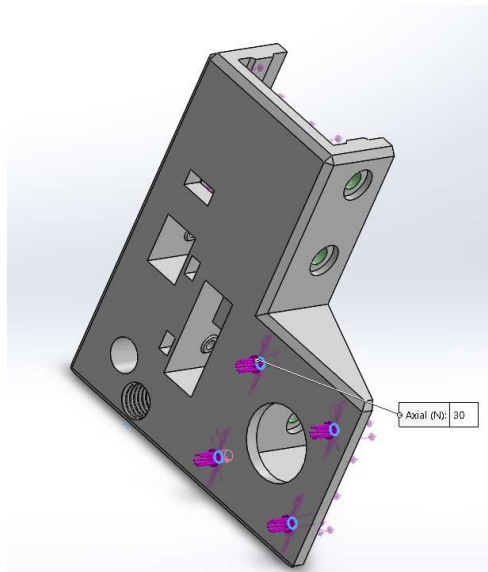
Carga axial de 30 N que sufren los tornillos del motor.
